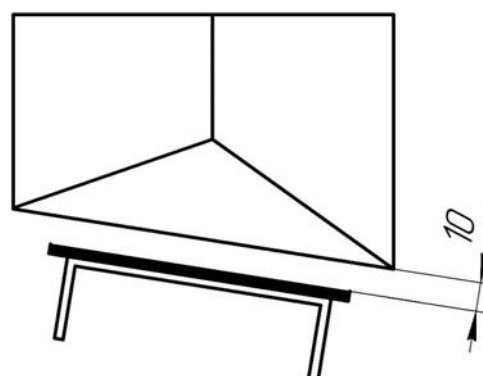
Установка зазора между направляющими оборачивающей ленты и боковой поверхностью колка
